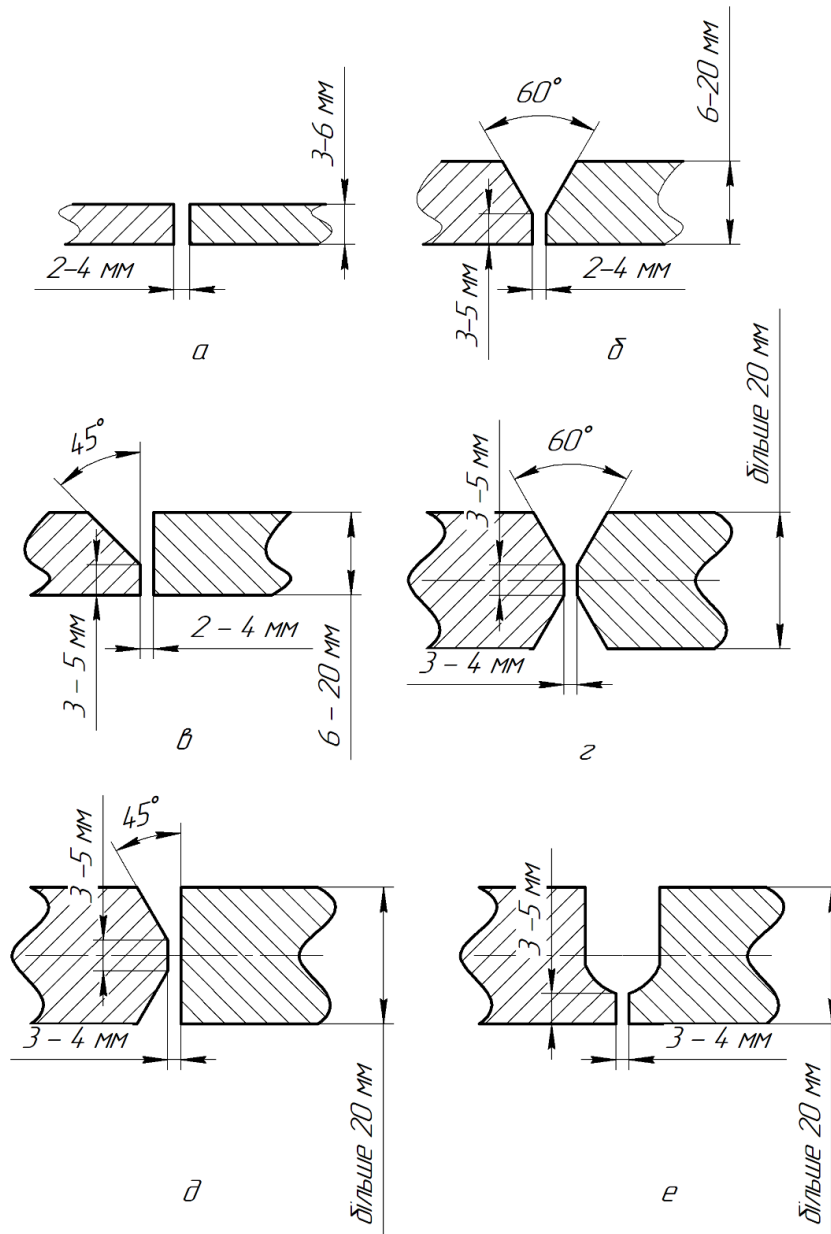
Підготовка крайок для ручного дугового зварювання в стик.
